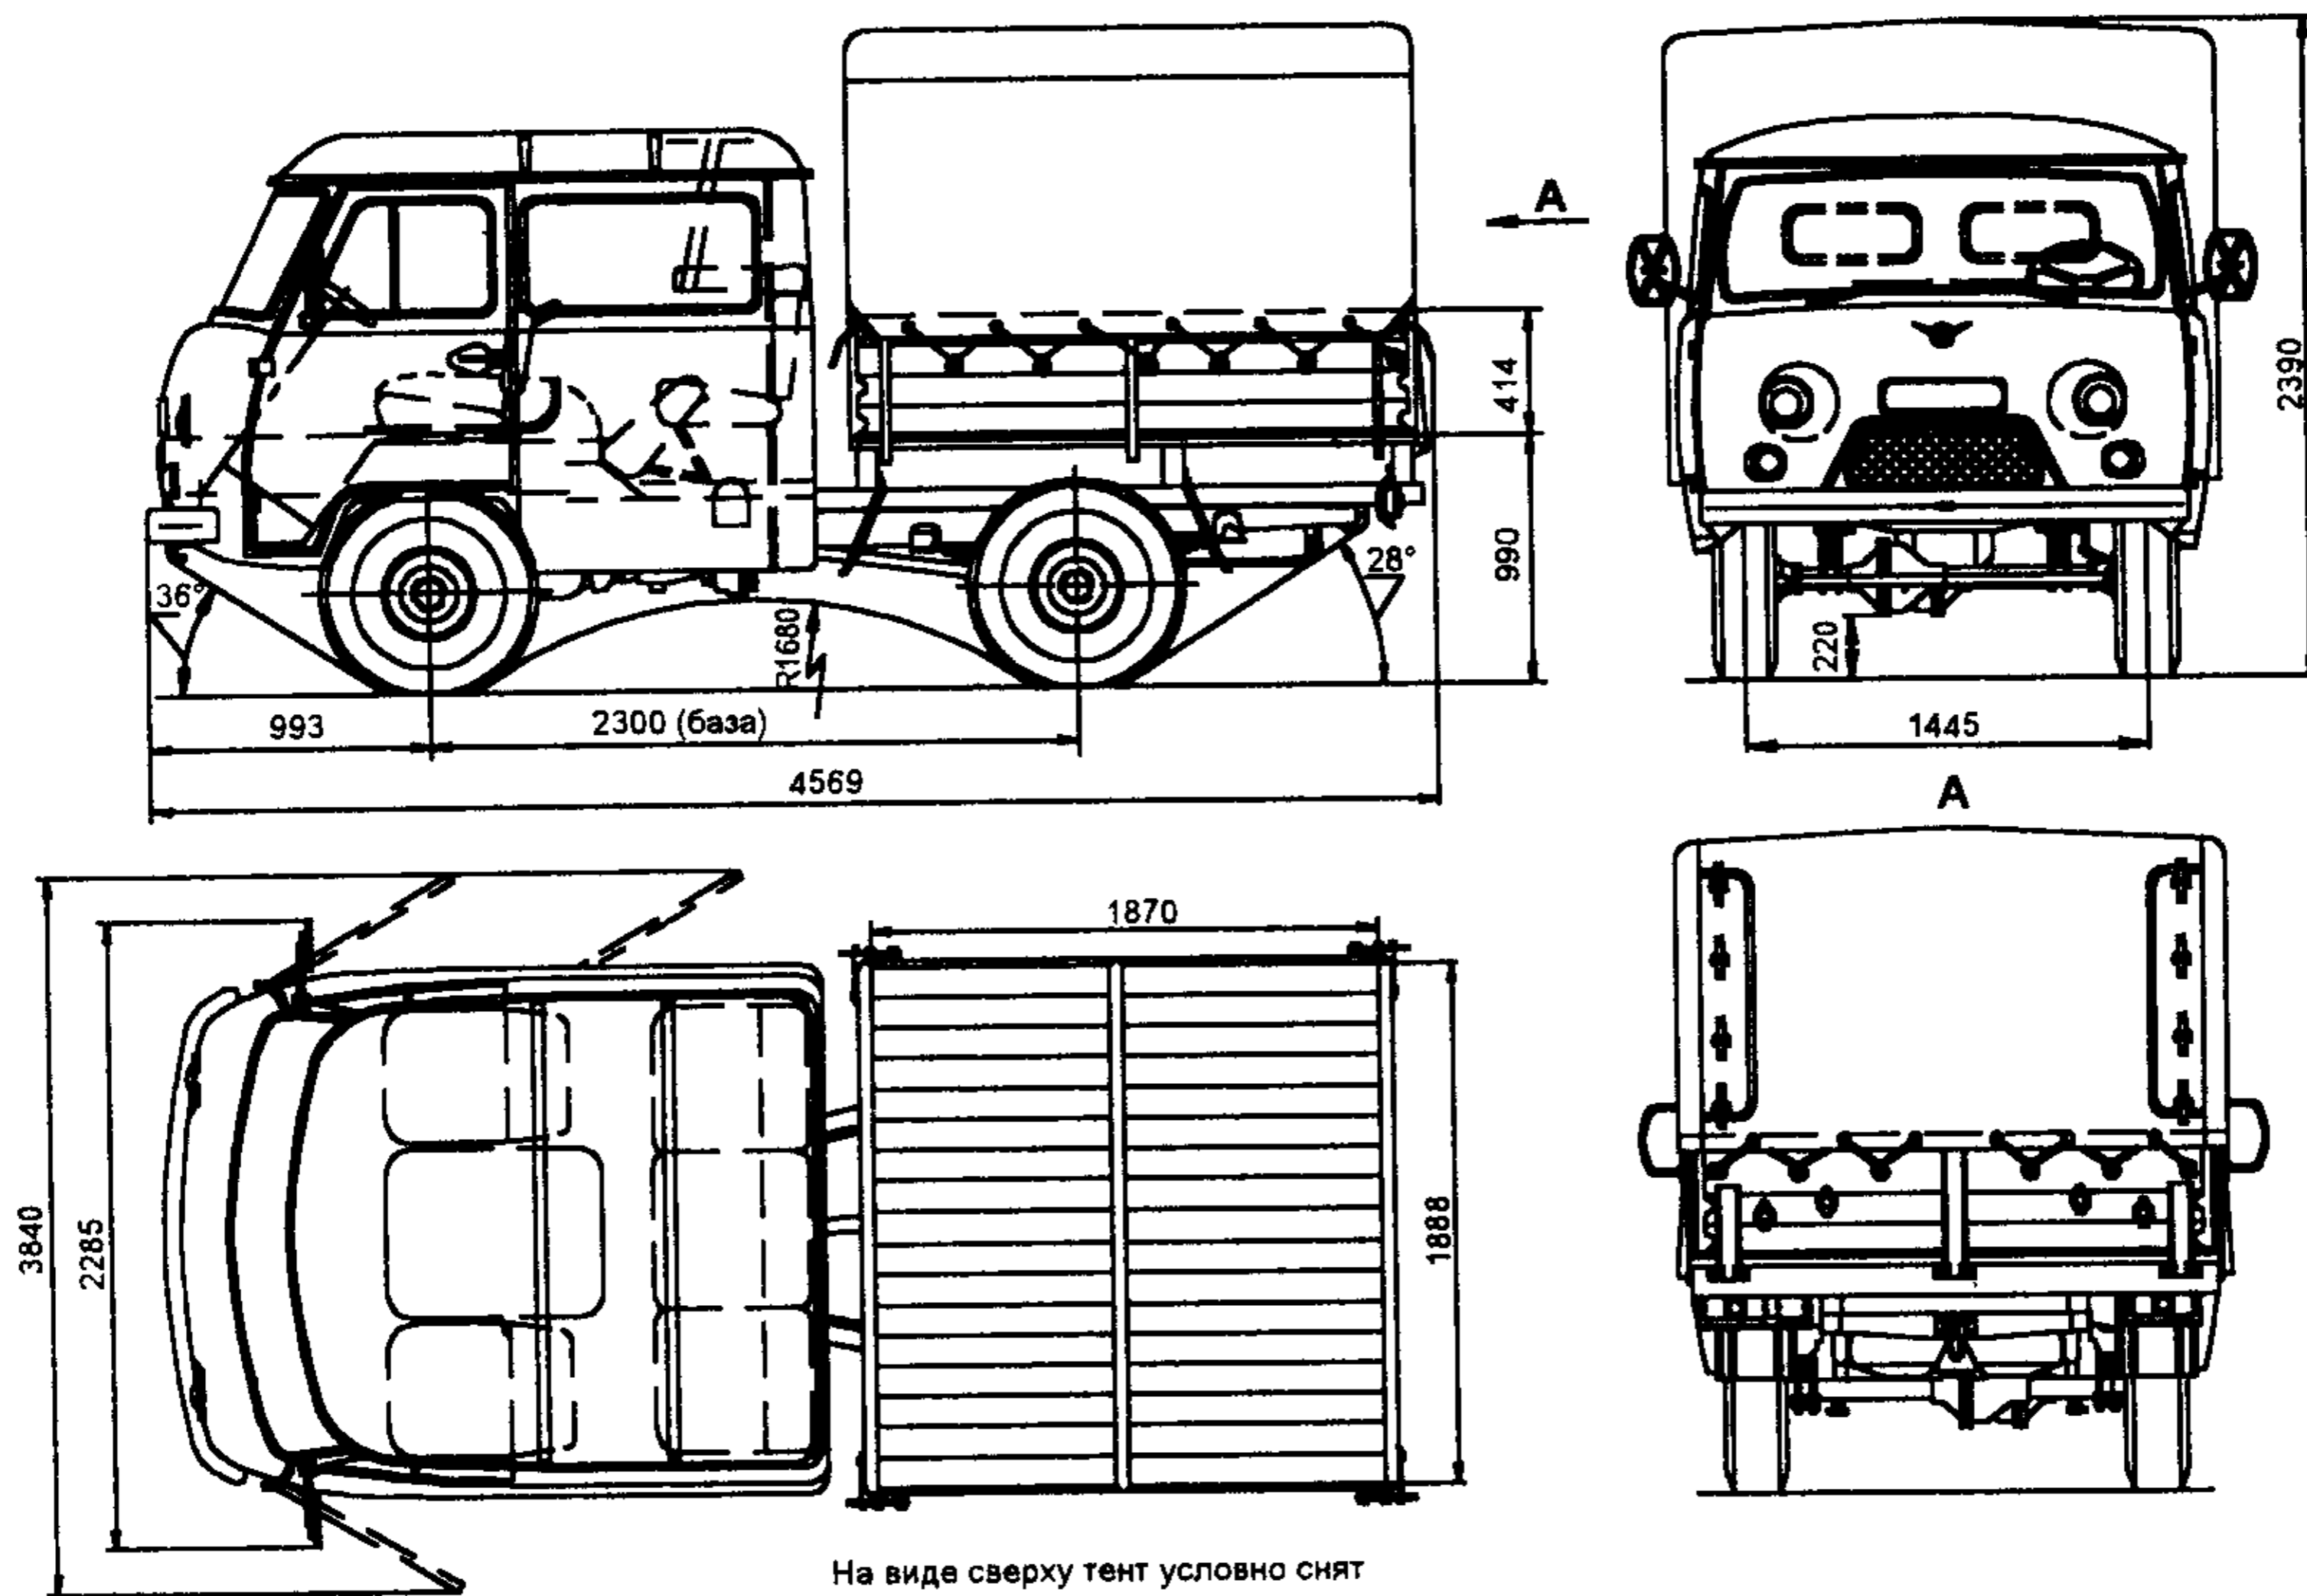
г. Основные размеры автомобиля УАЗ-39091
